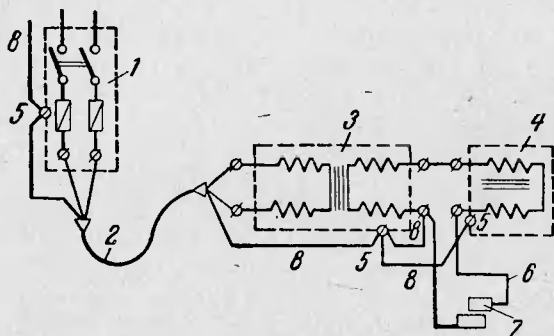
Схема подключения сварочного трансформатора.
